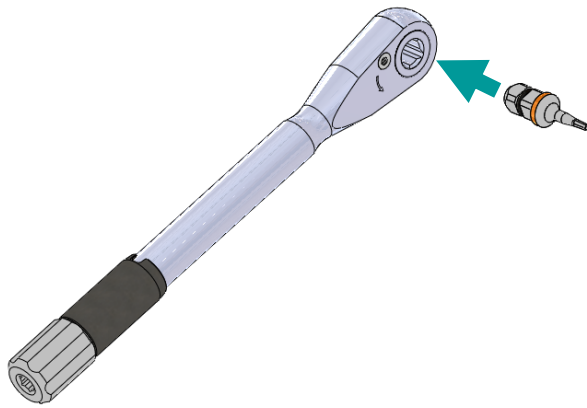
Ensamblaje destornillador-llave dinamométrica
